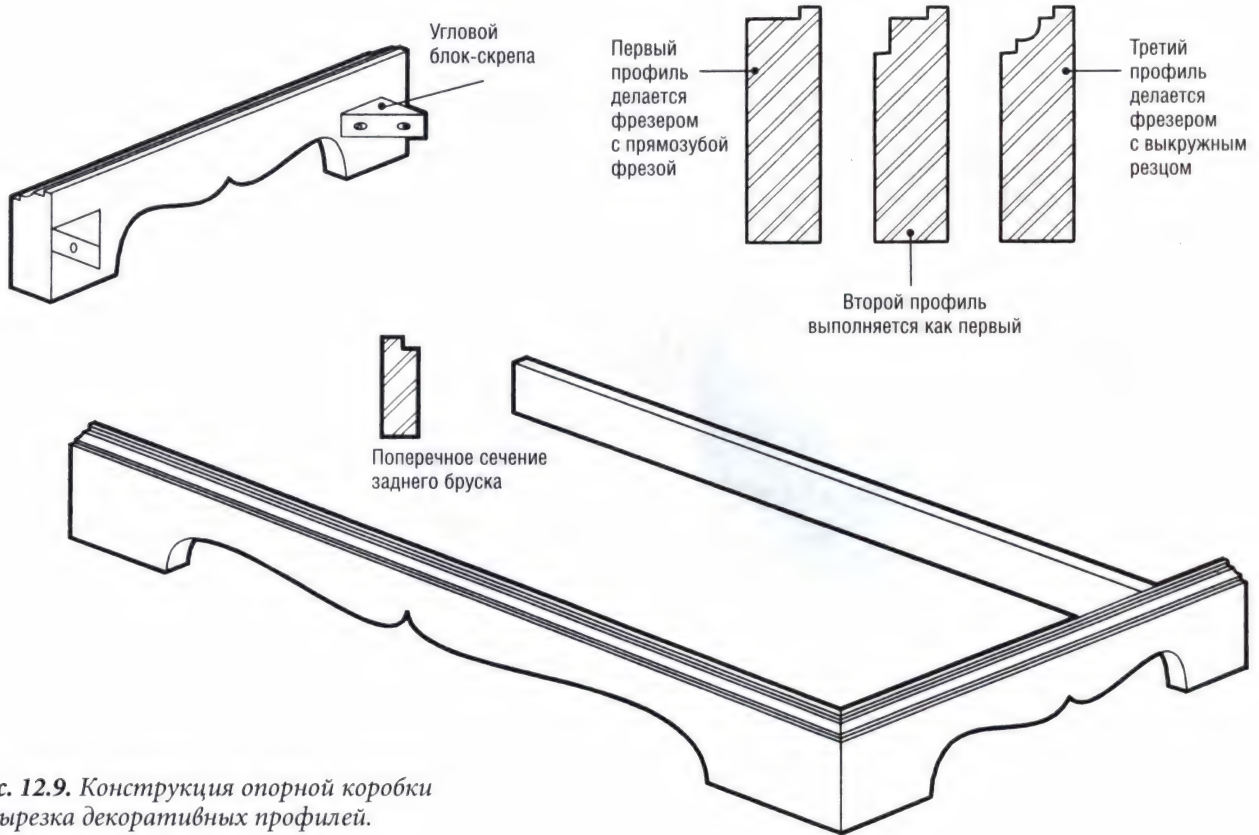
Конструкция опорной коробки и вырезка декоративных профилей.
